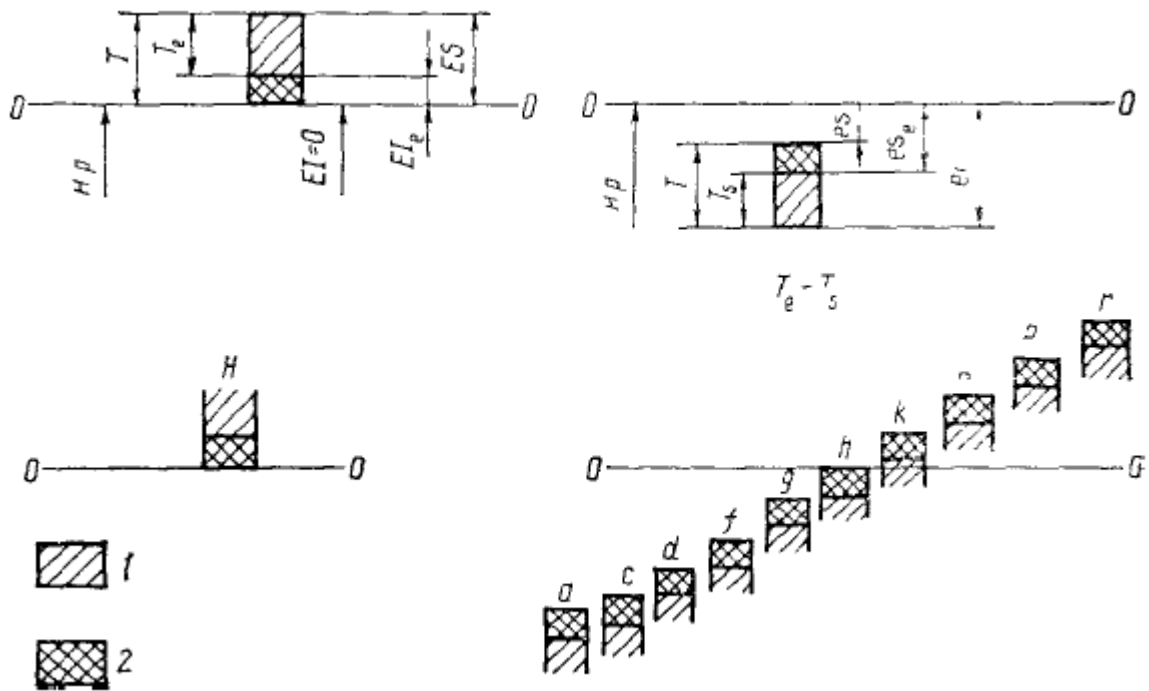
Поля допусків з'єднання шліцевого евольвентного
